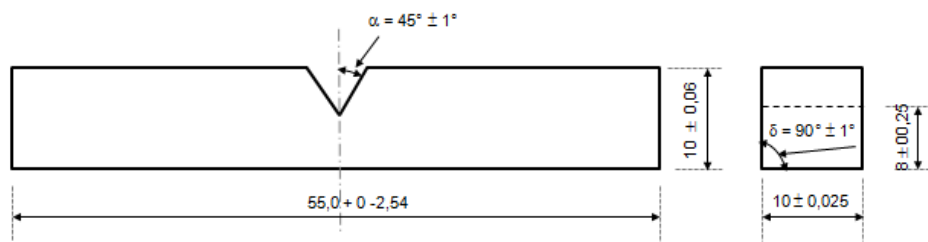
Dimensões do CP de Charpy conforme ASTM A-370 [17].
